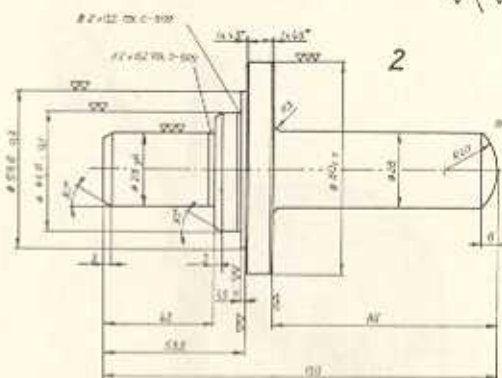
Einpressen des Wellendichtringes in das Schwenklager (W-210 747)
